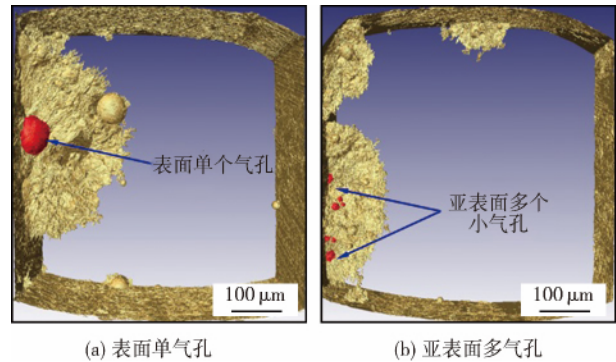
焊缝表面气孔导致的半椭圆裂纹
